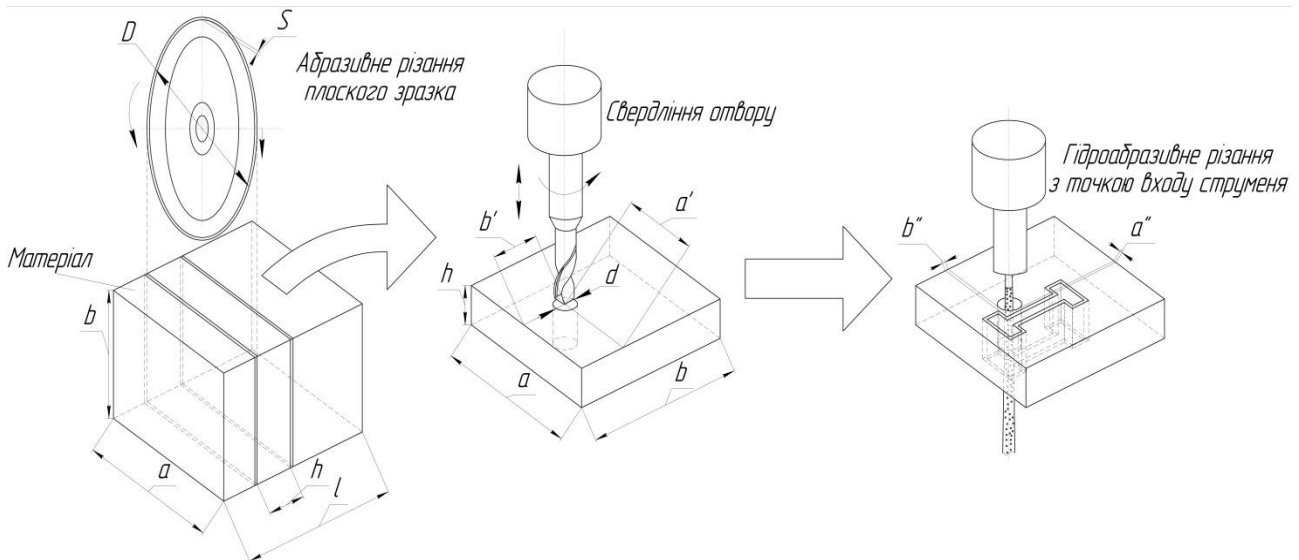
Послідовність підготовки зразка з карбової заготовки
